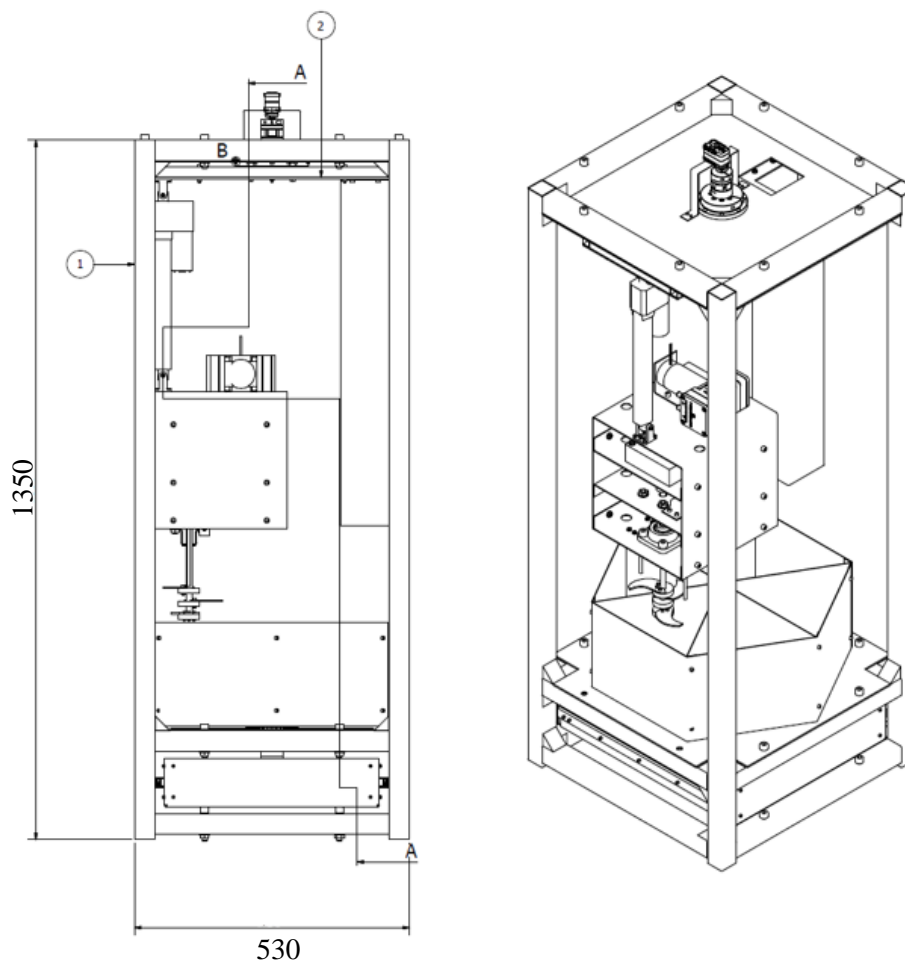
Vista isométrica a la derecha y vista frontal a la izquierda del ensamble general.
